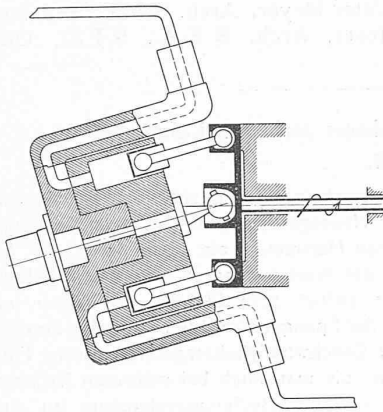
Ölpumpe der Hobelmaschine von H. A. Waldrich, Siegen i. W.
